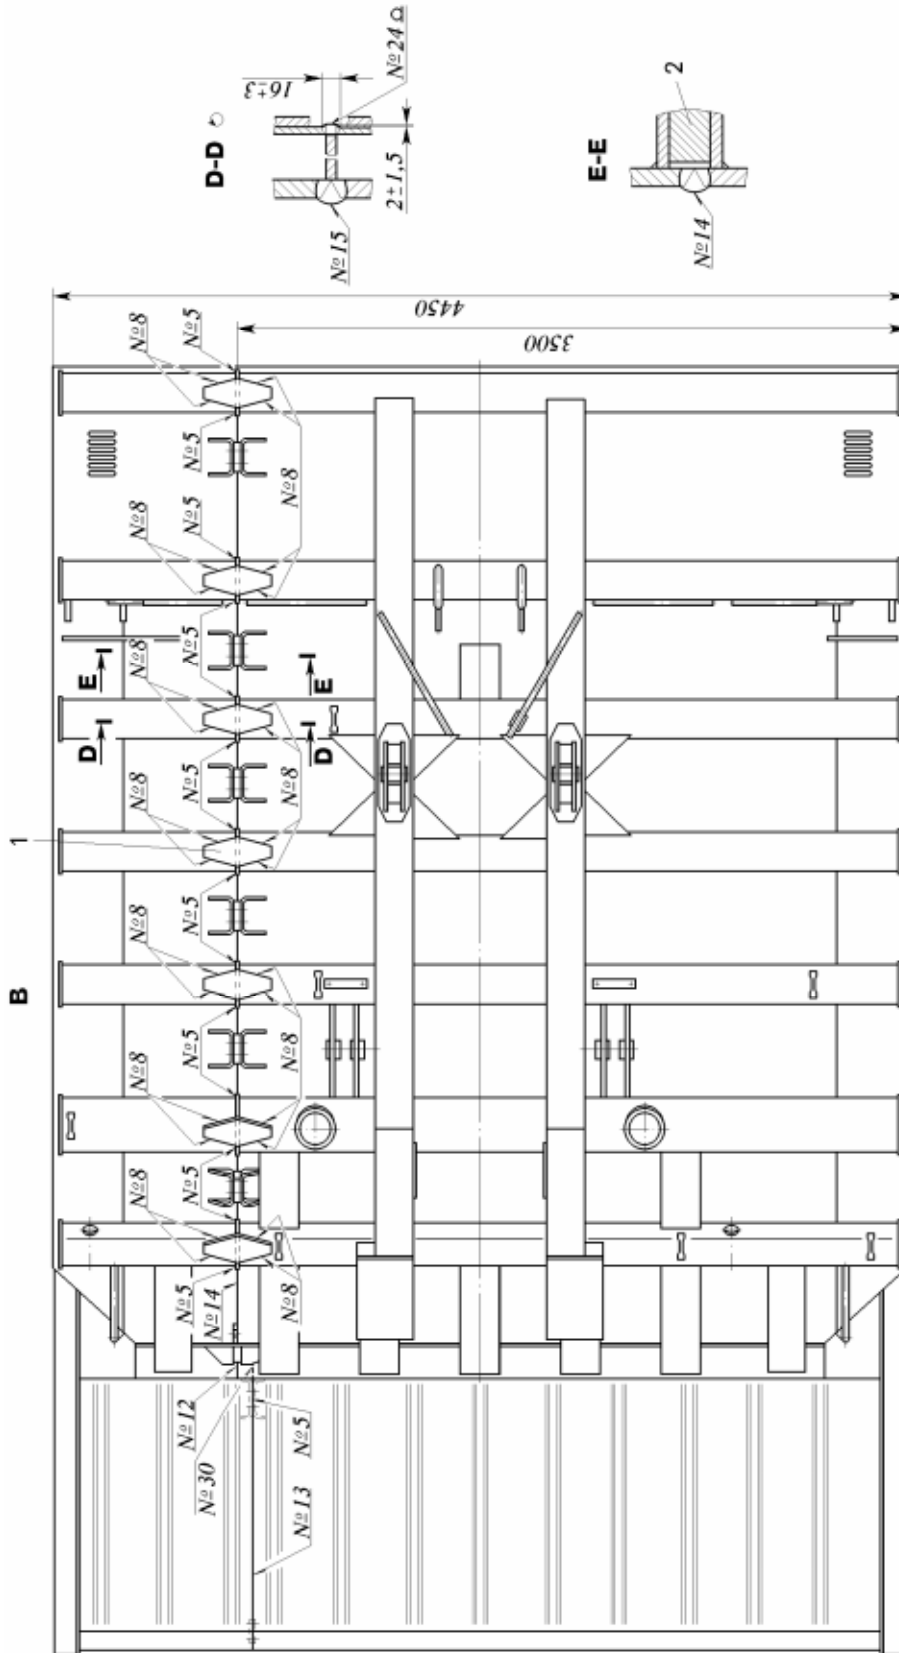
Сборка и сварка платформы самосвала–углевоза БелАЗ–75479 Вид В
